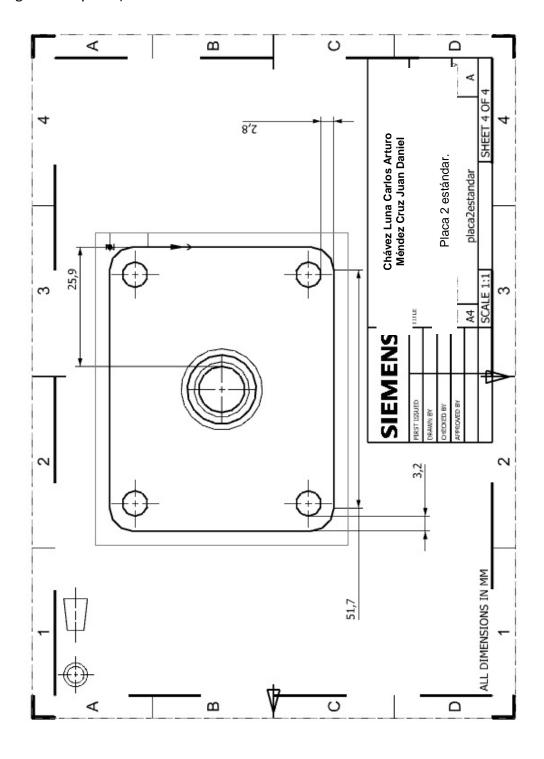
Plano pieza 2 estándar medidas actualizadas vista 1.
